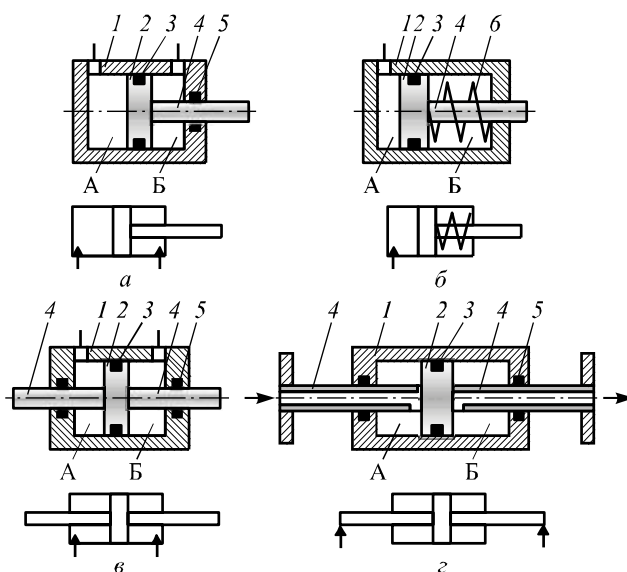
Конструктивные схемы и условные графические обозначения поршневых гидроцилиндров:
